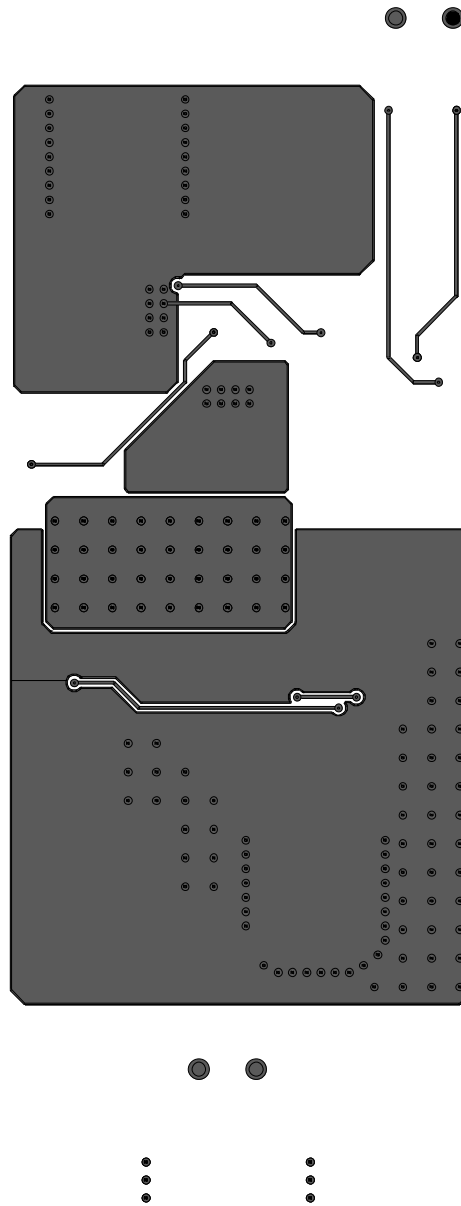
+3,3V-omvandlare lager 3 helt jordplan
